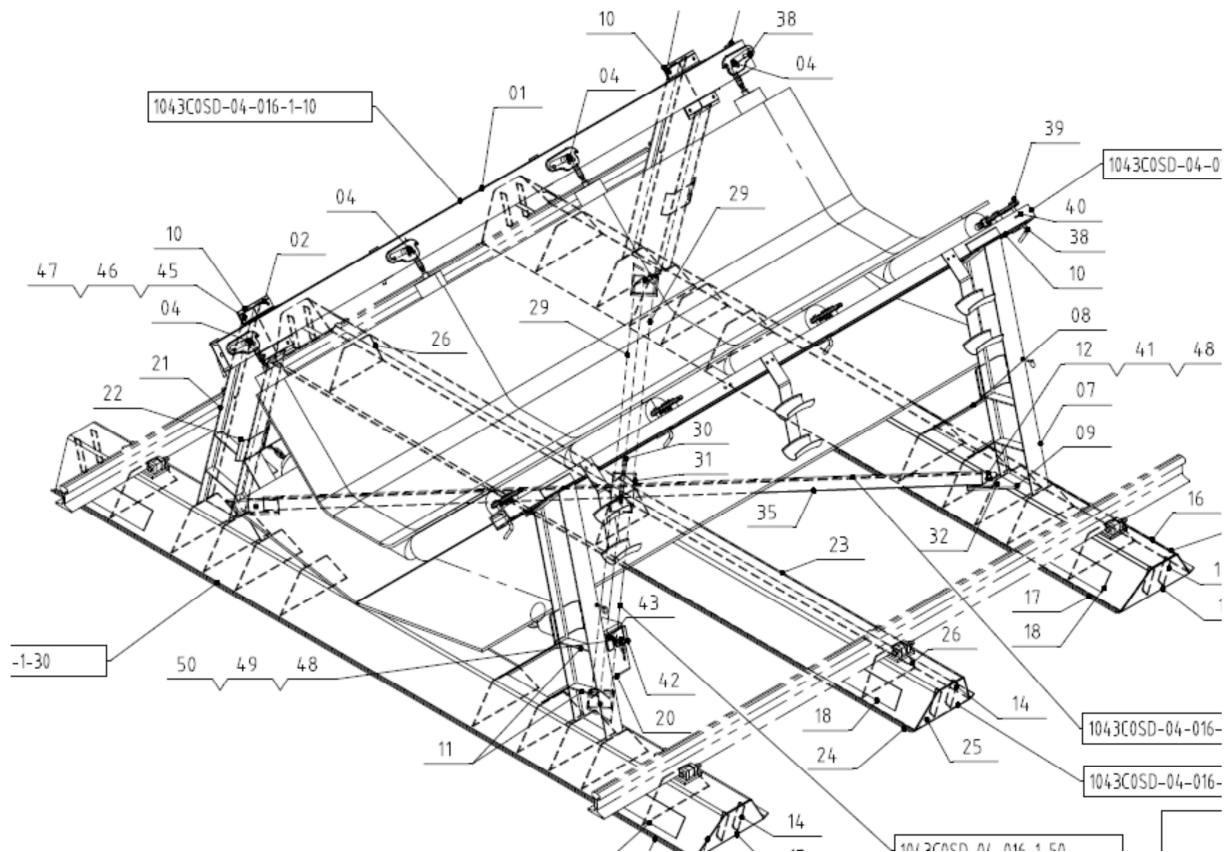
Standard Belt Frame 2.400 mm mit Stahlschwellen
